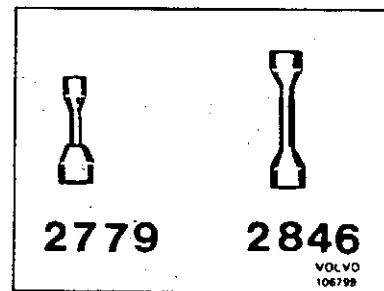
Werkzeug 999 2779 und 2846, Ausbauhülse für Gelenkwelle
